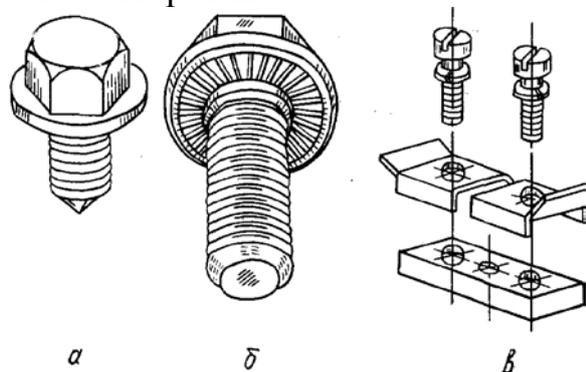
Технологичная конструкция резьбовых деталей:
